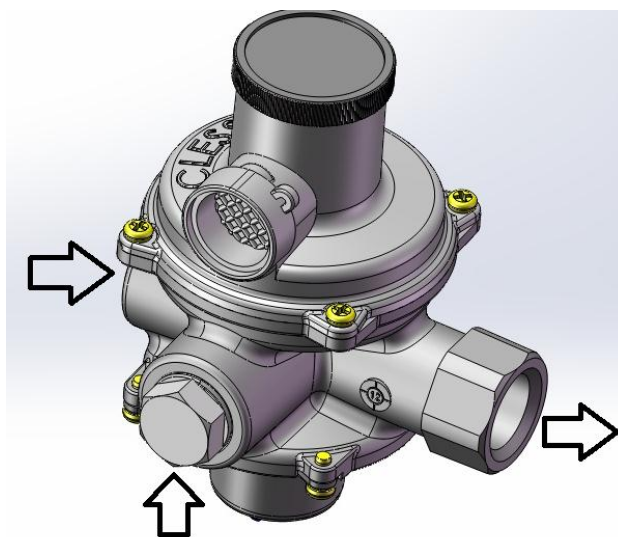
Regulador Tecnix OPSO com montagem em linha
